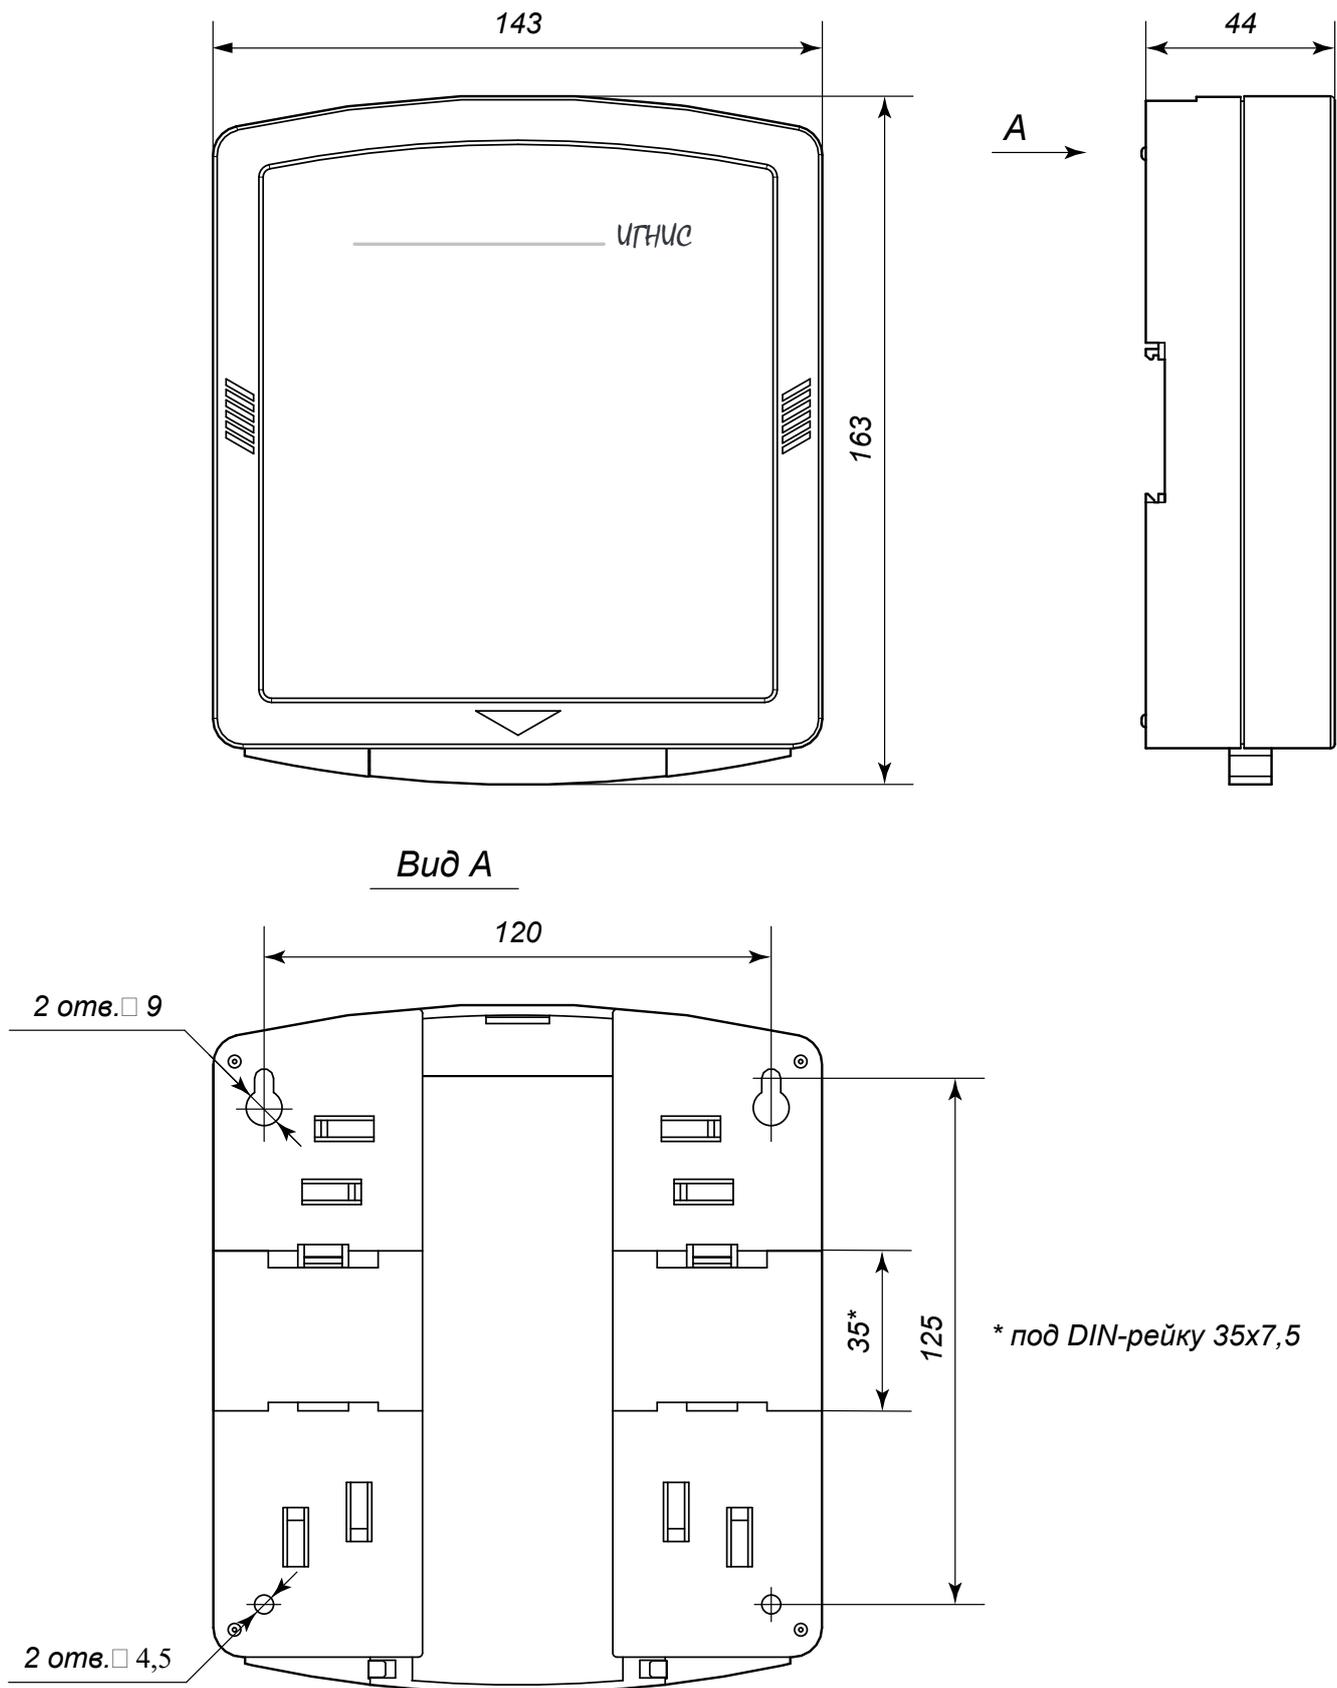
Габаритные и установочные размеры устройств ААКПС, МША, МКП
